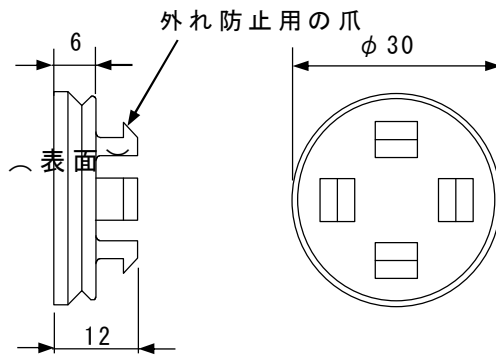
注入孔カバーの例 写真-2.2.10 注入孔カバーの例
